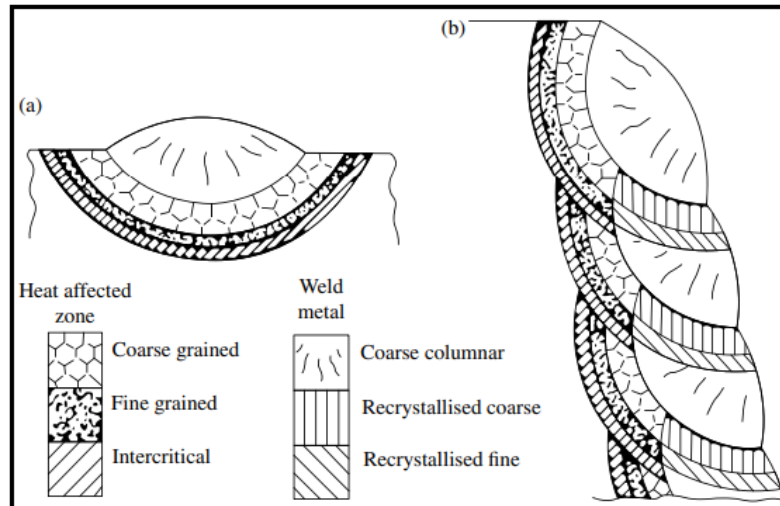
Evolución microestructural de la ZAC en a) soldadura de un cordón y b) soldadura a tope con superposición de cordones, (LIPPOLD, 2015).
